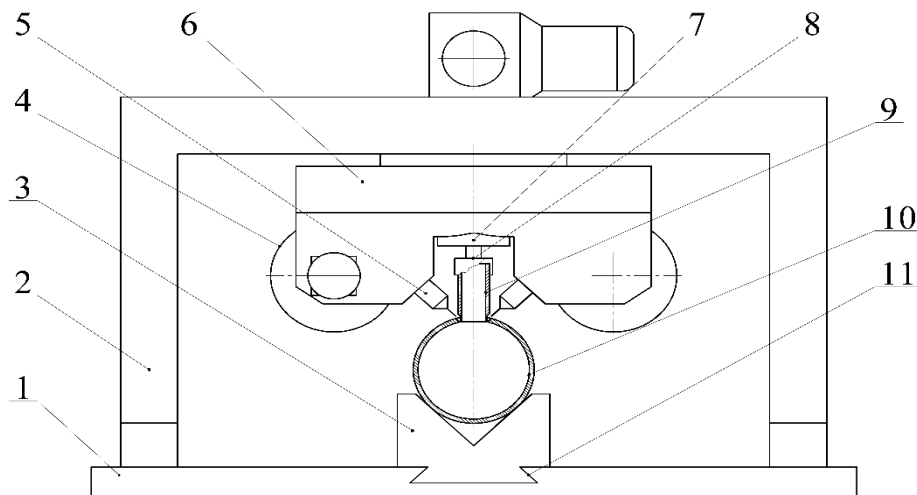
Установка для механизированной прецизионной сварки коллекторов
